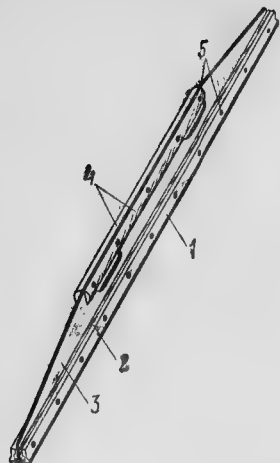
1 — корпус; 2 — ампулы; 3 — крышка
